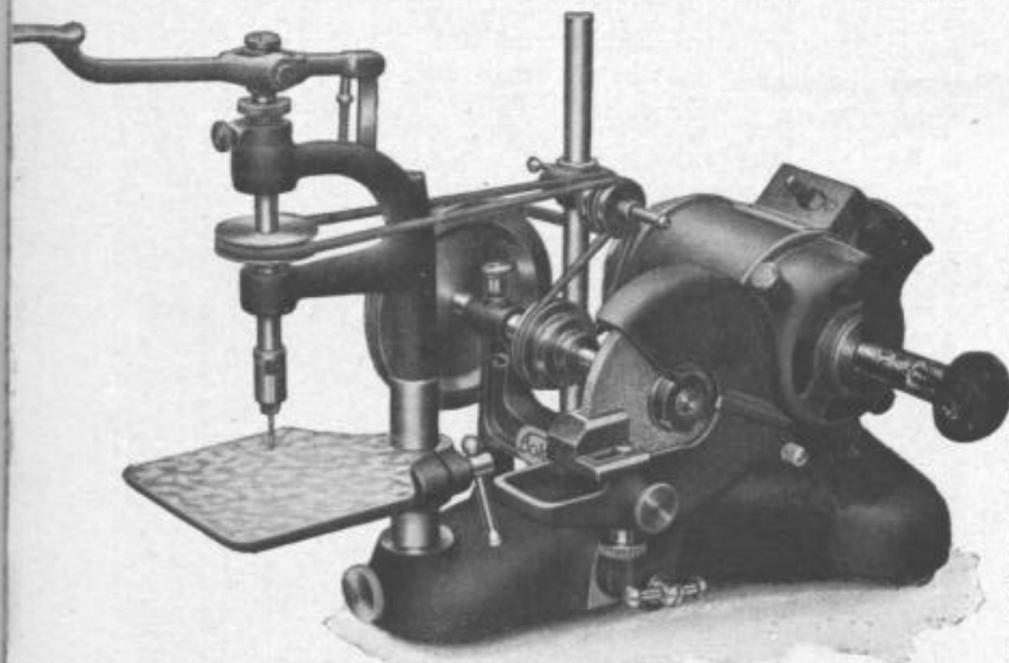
Die „Schwerfußwerkstatt“, Schwerfußmotor mit angebauter Bohrmaschine, Schleifscheibe und Polierspindel
